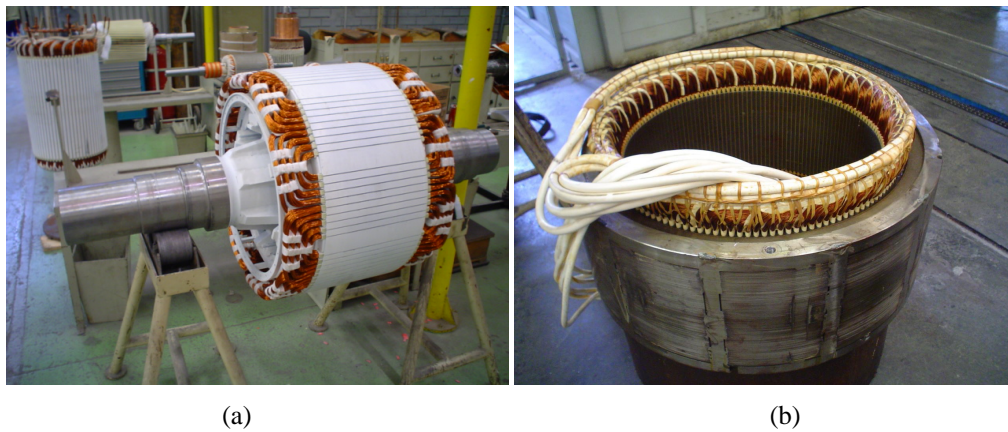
(a) Rotor bobinado, (b) Estator bobinado.
